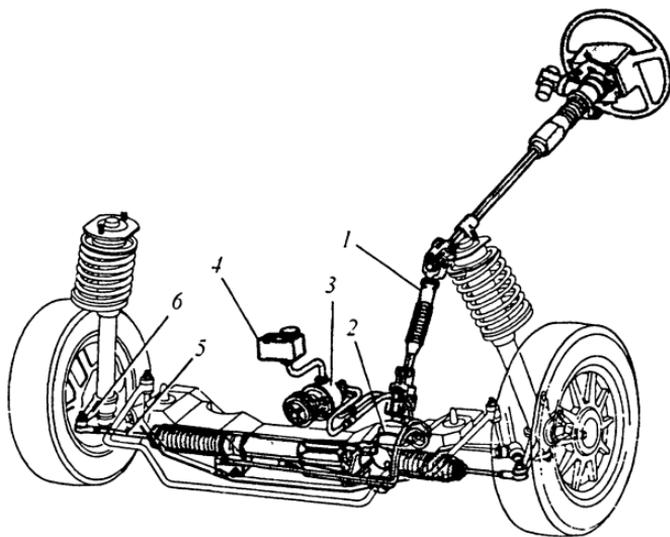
Детали механизма рулевого управления с гидравлическим усилителем (автомобиль с левым рулем): 1 — промежуточный вал; 2 — рулевая передача; 3 — насос; 4 — бачок с рабочей жидкостью; 5 — поперечная рулевая тяга; 6 — маятниковый рычаг
